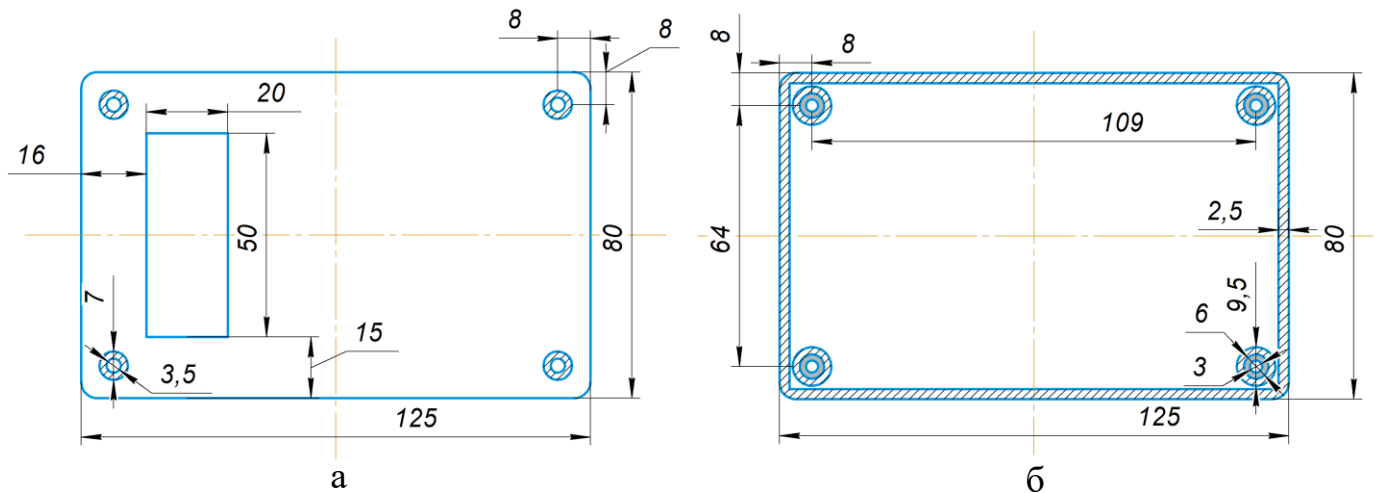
Нижня половина корпусу вид ззовні (а), вид з середини (б)
